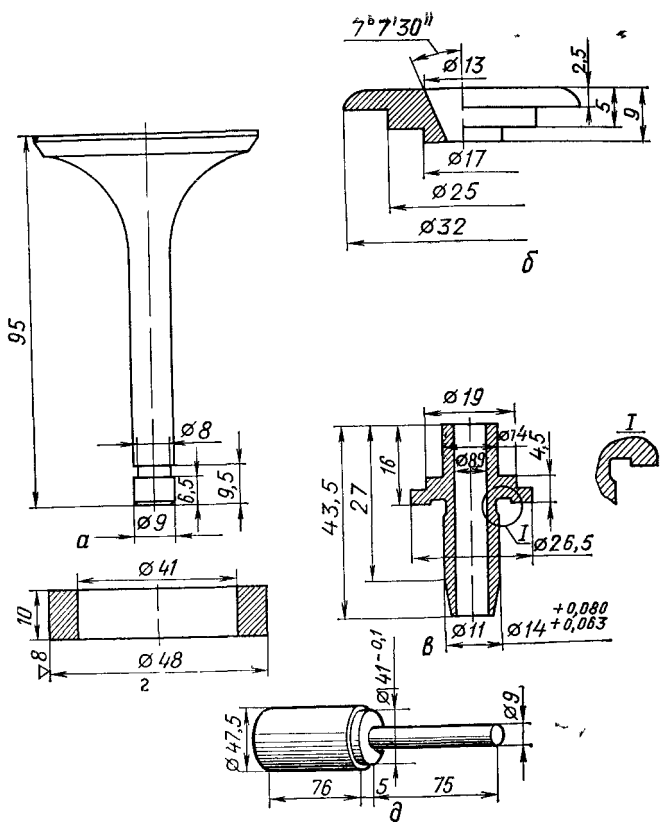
Детали узла впускного клапана двигателя Д-3 и оправка:
